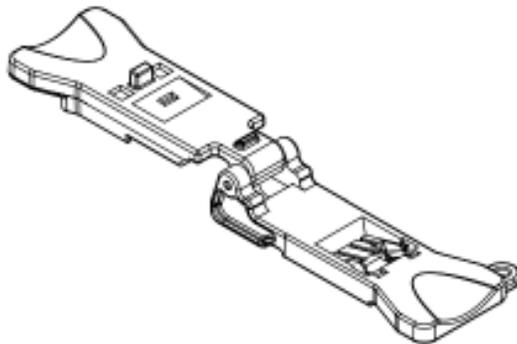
Ponchadora propietaria Panduit (Panduit, Panduit, 2004)
